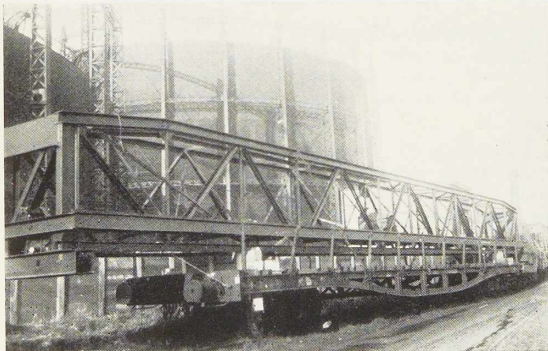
Poutre principale d'un pont roulant soudé.
